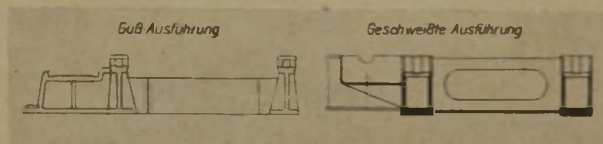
Gewichtsvergleich einer Guß- und Schweißkonstruktion des Rollgangrahmens eines Blocktransport-Rollganges. Gewicht der Gußausführung 4100 kg, Gewicht der geschweißten Ausführung 3200 kg, Gewichtsersparnis 22 Prozent
